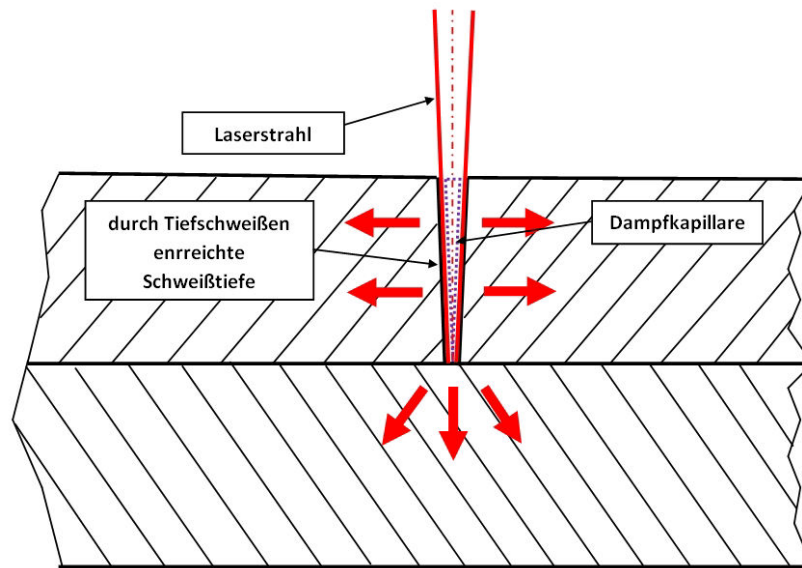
Ausbildung der Schweißnaht im Aluminium
